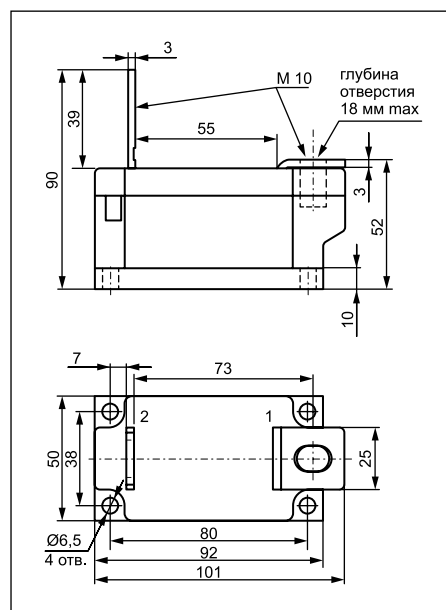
Габаритный чертеж модуля М1ДЛ-400
